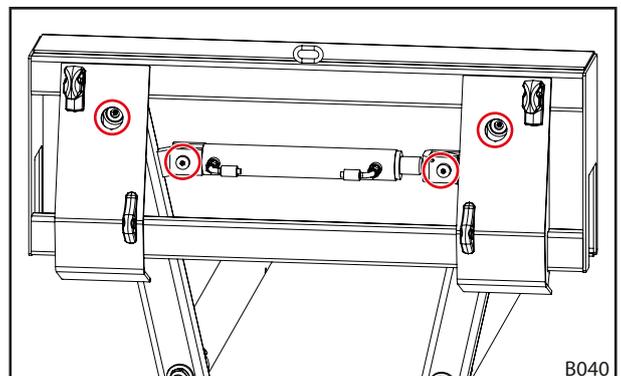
Puntos de engrase de la horquilla de rodillos para pacas
